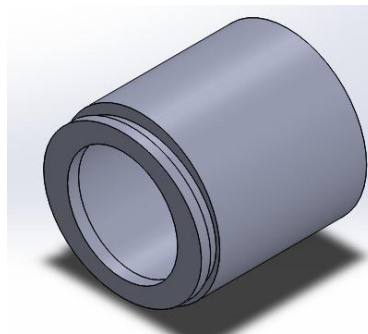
Acople para el desvío de gases del exosto hacia el banco de sensores, diseño en Solidworks. Elaboración propia.
